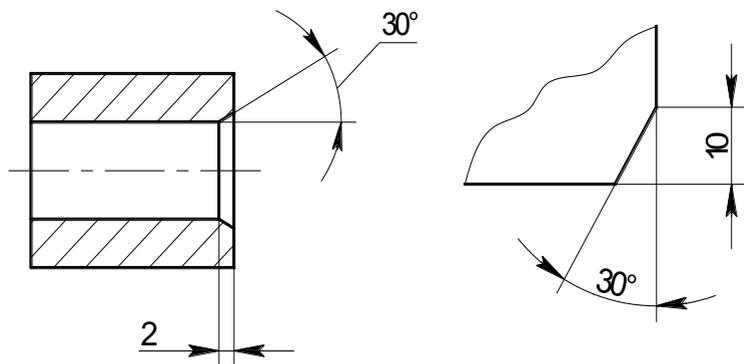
Нанесение размеров фасок линейными и угловыми размерами
